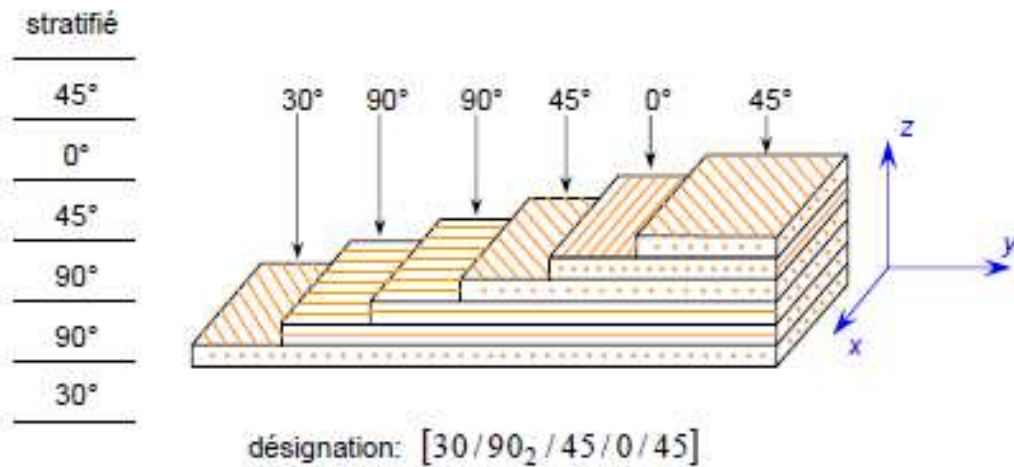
Exemple du plan du drapage d'un composite stratifié
